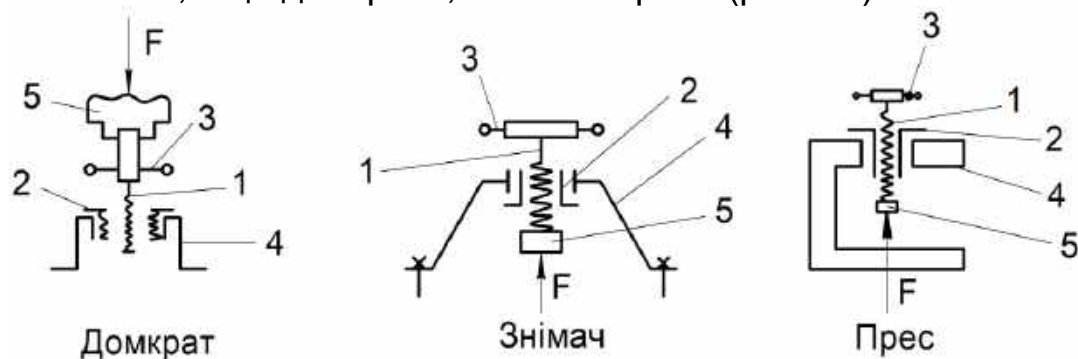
Схеми пристроїв, в яких застосовується передача гвинт – гайка з тертям ковзання: 1 – гвинт; 2 – гайка; 3 – рукоятка; 4 – корпус; 5 – башмачок
